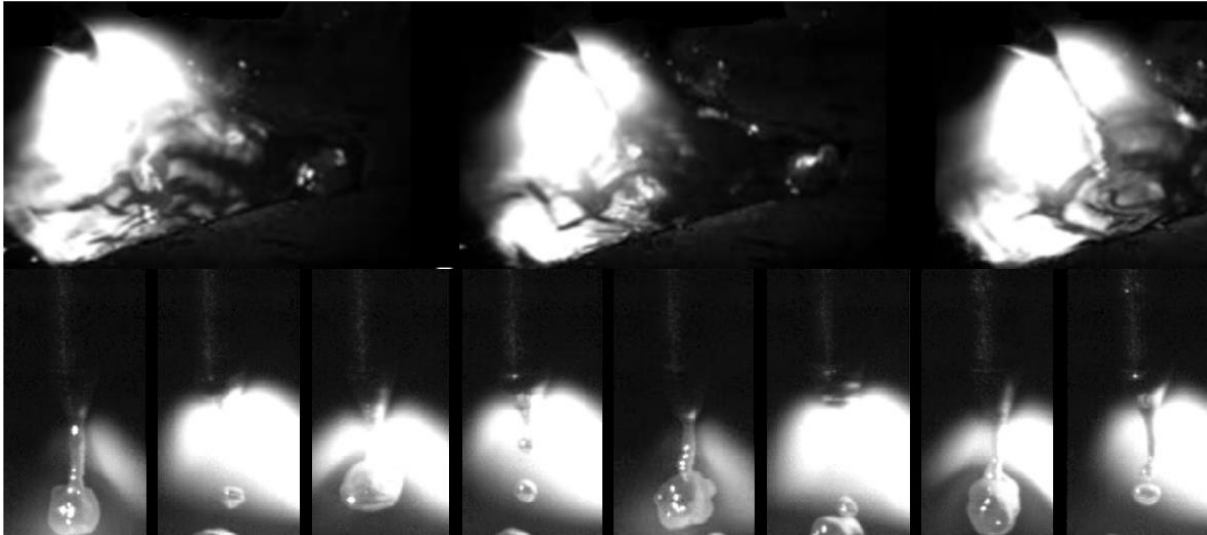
Ejemplos De Transferencia Pulverizada En Soldadura [33 y 34].
